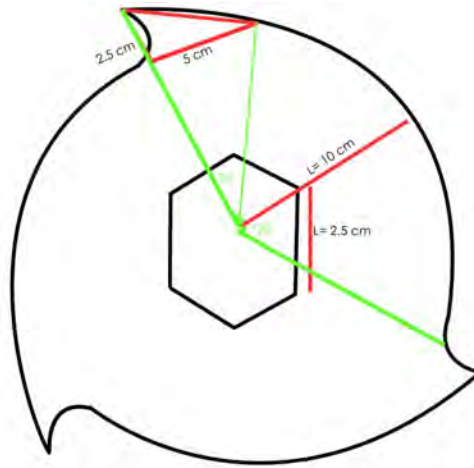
Dimensiones geométricas iniciales de cuchilla. Fuente: Elaboración propia
